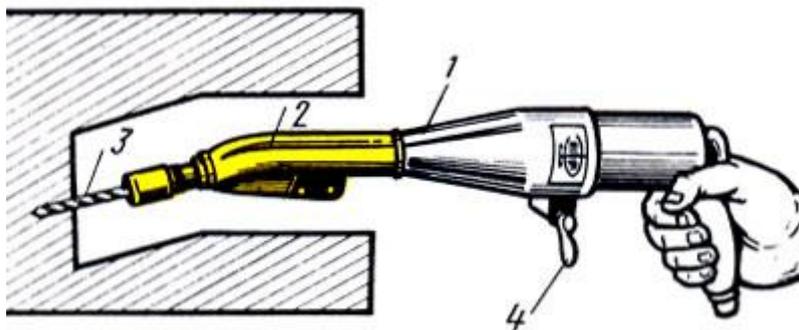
Пневматическая сверлильная машина PCS с угловой насадкой:
